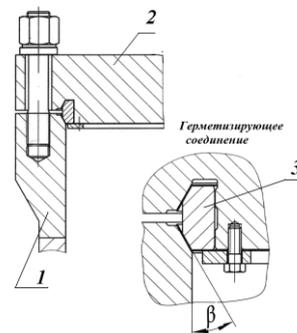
РС с двухконусным уплотнительным кольцом: 1 — соединяемая деталь (корпус); 2 — соединяемая деталь (крышка); 3 — уплотнительное кольцо
